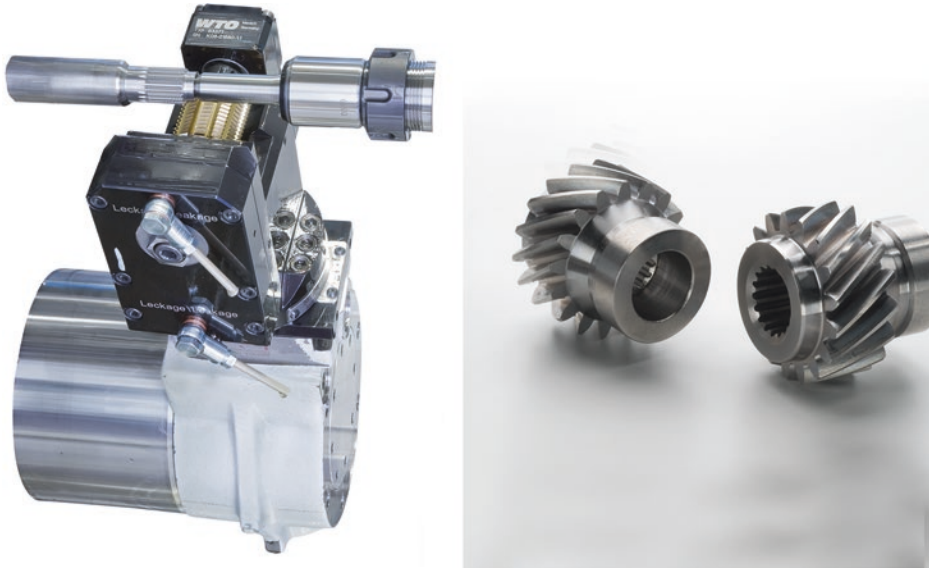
Wälzfräseinrichtung auf einem CNC-Mehrspindel-Drehautomaten (links) [Schu16a] und auf einem CNC-Mehrspindler gefertigte Beispielwerkstücke (rechts) [Inde15b]
